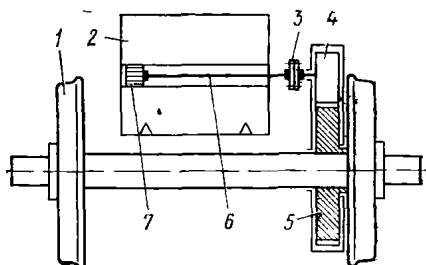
Схема опорно-рамного привода с карданным (торсионным) валом:
